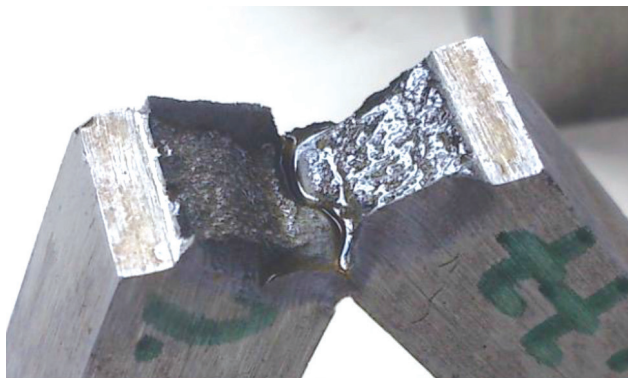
Superficie de fractura ASTM A36 a 60°C.
